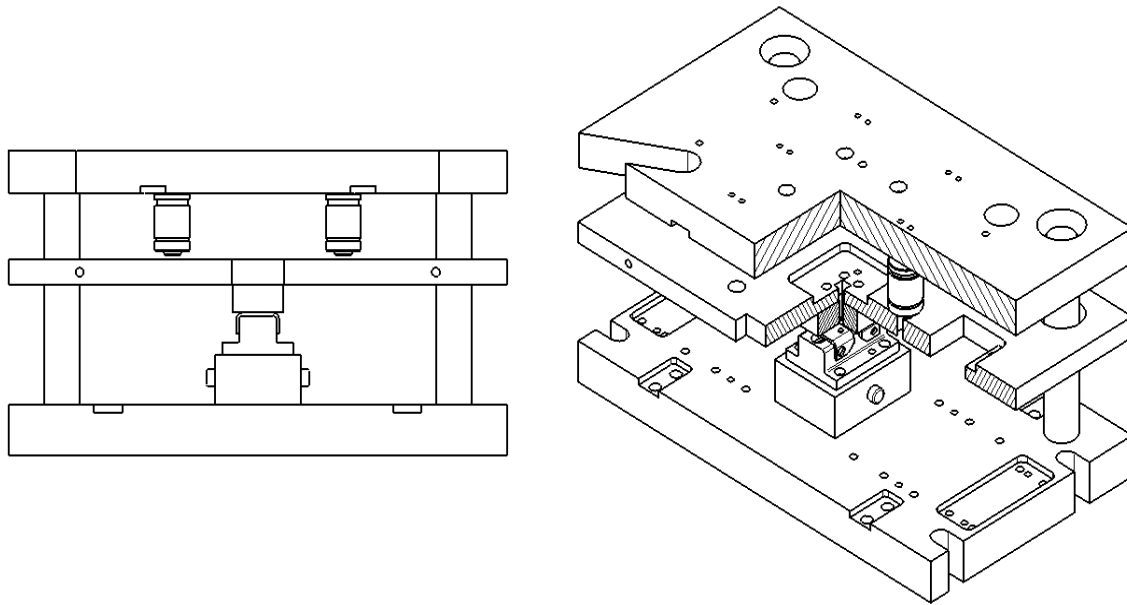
Placas superior, pisadora e inferior y guías.
